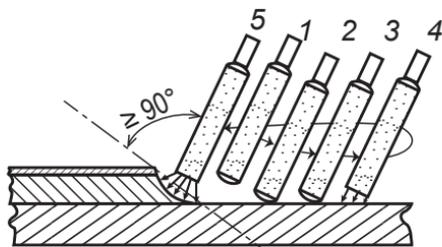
Зажигание сварочной дуги для продления сварочного шва
